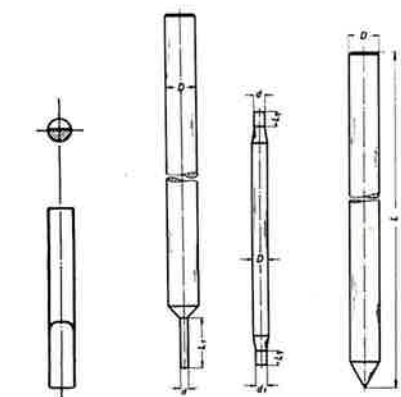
Halbfräser für Gm 03 D (Halbfabrikat)
